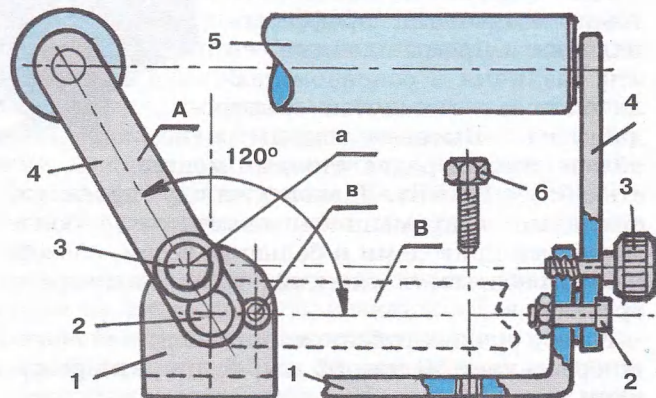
Устройство ручки: А — рабочее положение; а — место расположения резьбы для фиксатора. В — положение для переноски; в — место расположения резьбы для фиксатора. 1 — крепежная скоба; 2 — ось; 3 — фиксатор; 4 — скоба ручки; 5 — рукоять; 6 — крепежный винт.
